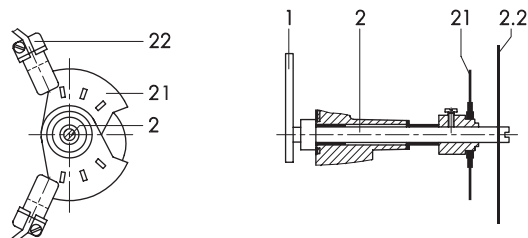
· Исполнение с двумя индуктивными конечными выключателями
